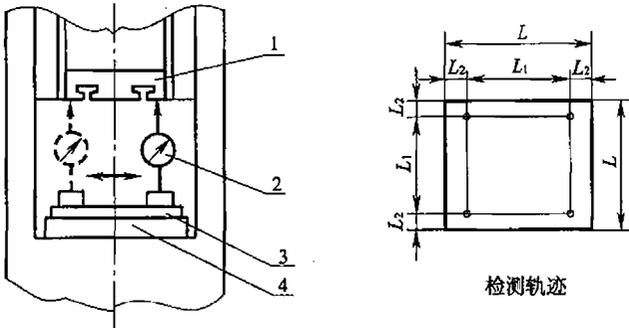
检验滑块下平面与工作台上平面的平行度
